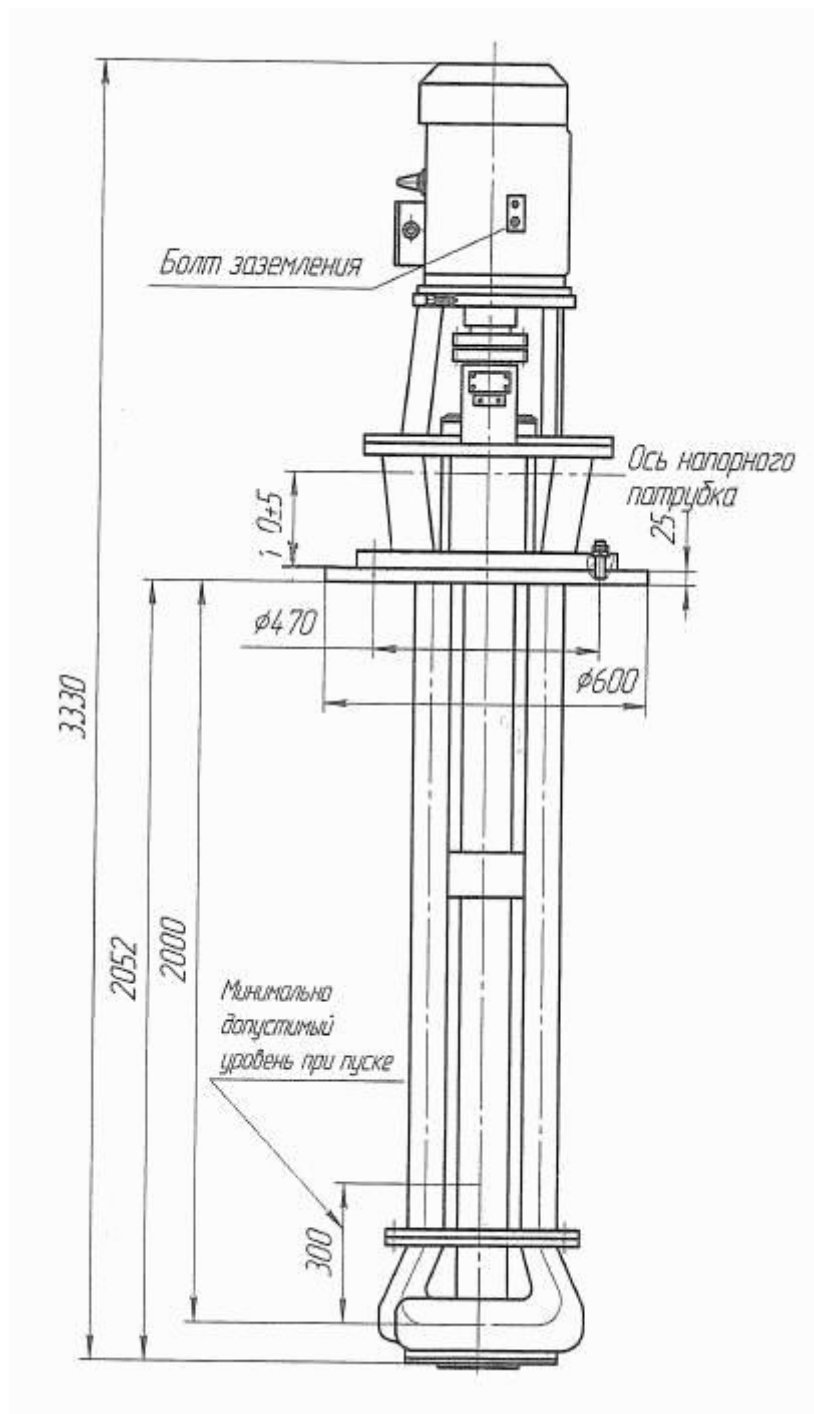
Габаритный чертеж насоса дренажного бака
